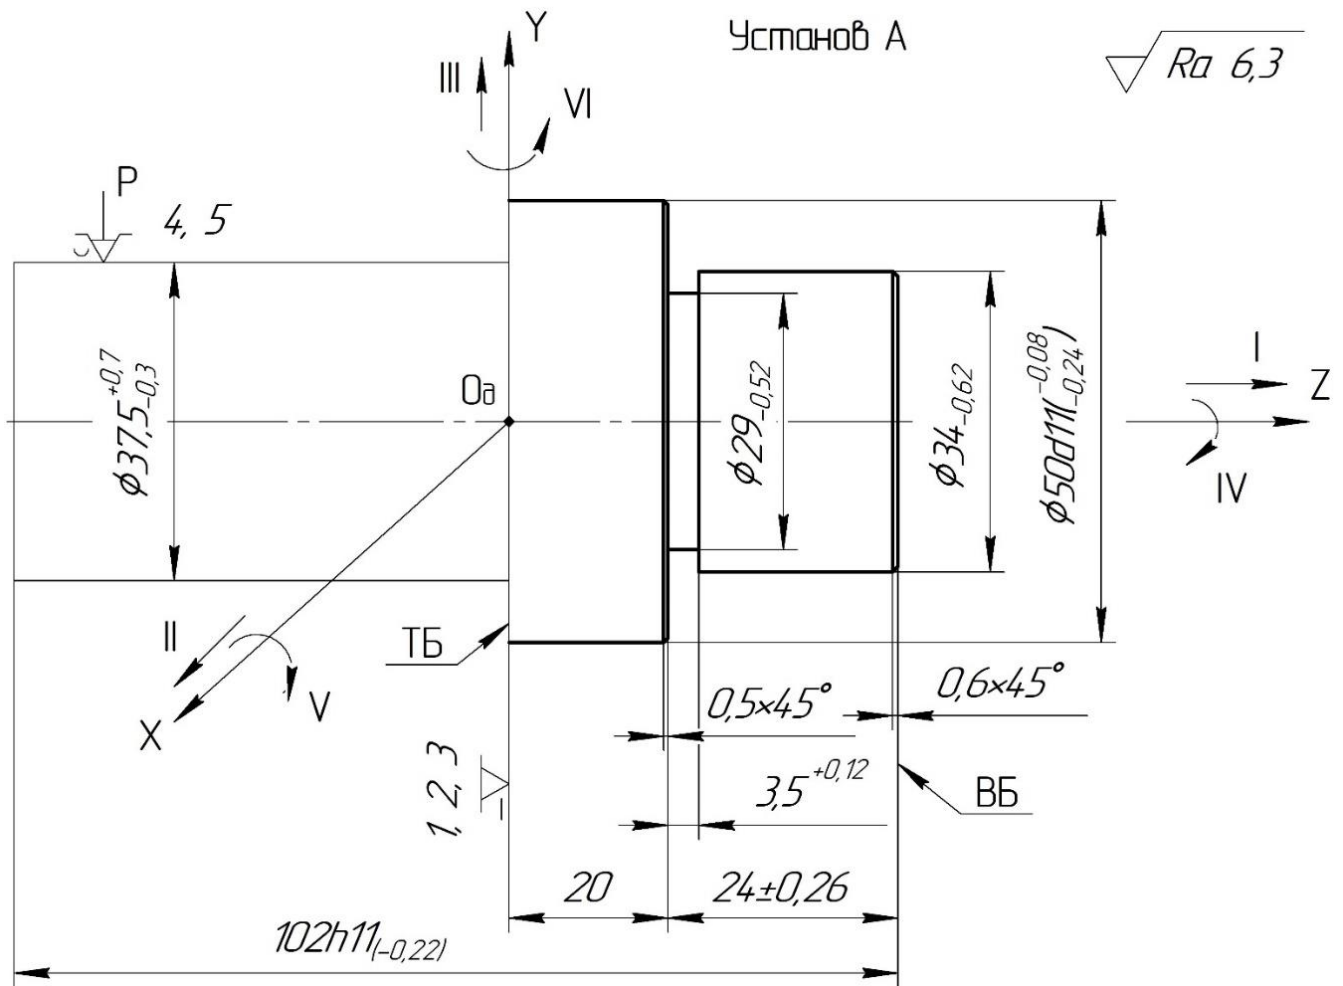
Базування заготовки на операції 015 «Токарна з ЧПК». Схема №2
